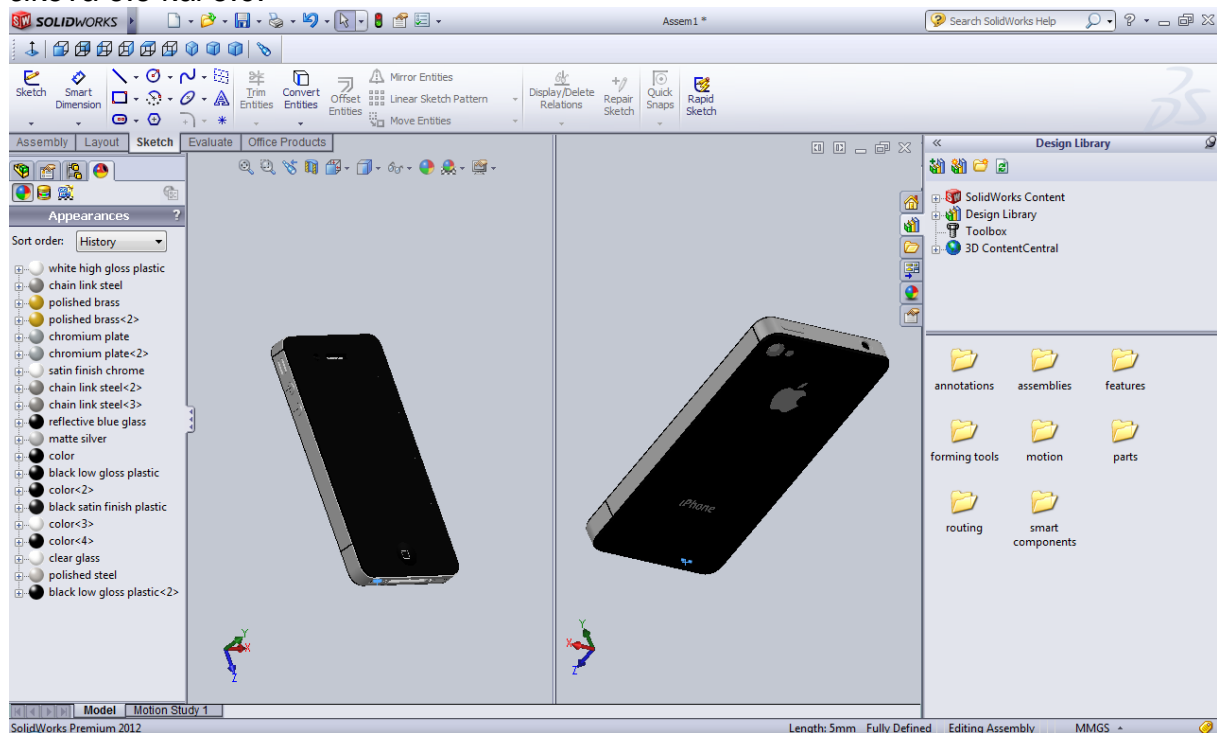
Πρώτα από όλα γίνεται η σχεδίαση μέσα από το 2d engineering drawing, typically of part or assembly.
